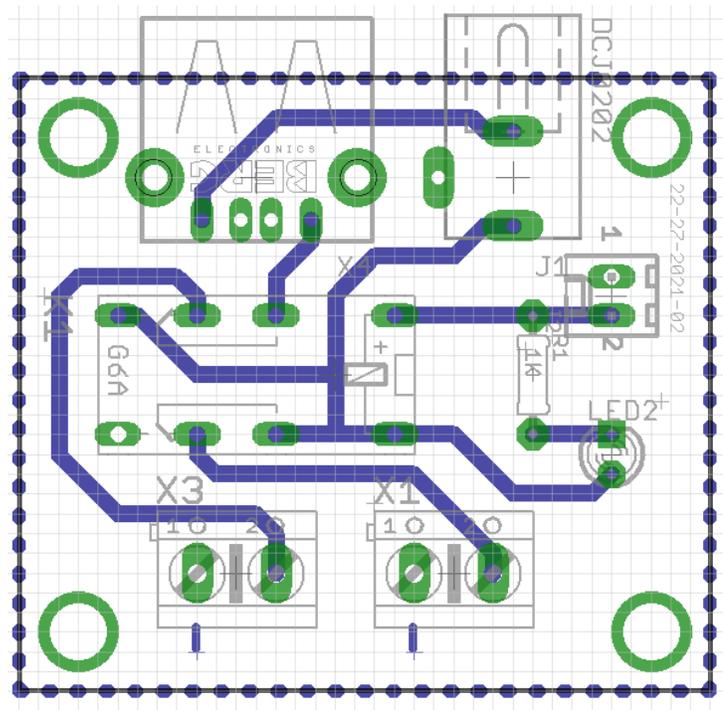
d Diseño del PCB del circuito de conmutación.
